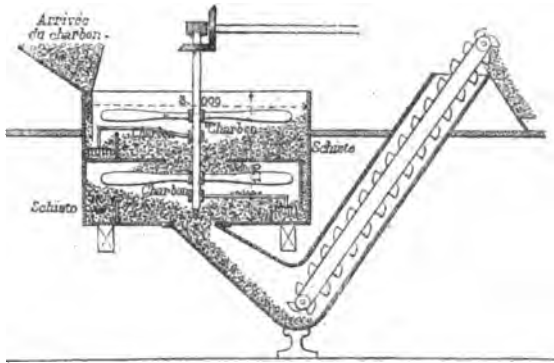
Lavoir Laporte et Jourjon (coupe verticale).
